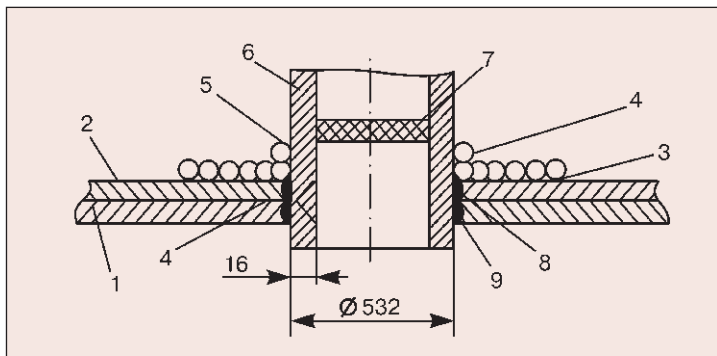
Схема установки электронагревателей КЭН при местной термообработке сварных соединений штуцера размером 532×16 мм: 1 — оболочка шарового резервуара; 2 — воротник штуцера; 3 — электронагреватели КЭН, размещенные на воротнике штуцера (первая зона нагрева); 4 — термоэлектрические преобразователи; 5 — электронагреватели КЭН, размещенные на штуцере (вторая зона нагрева); 6 — штуцер; 7 — теплоизоляционная заглушка на внутренней полости штуцера; 8 — сварное соединение воротника с оболочкой и штуцером; 9 — сварное соединение штуцера с оболочкой
